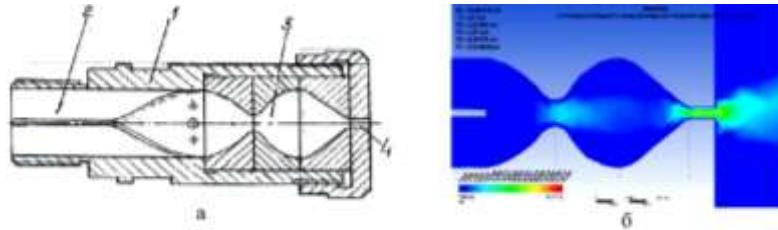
Схема кавітаційної форсунки та розподіл потоку мийочної рідини: (а) 1 – корпус; 2 – камера закруткі струменя; 3 – камера Лавалю; 4 – сопло; (б) – оцінка кавітаційного поля мийочної рідини з насадка
